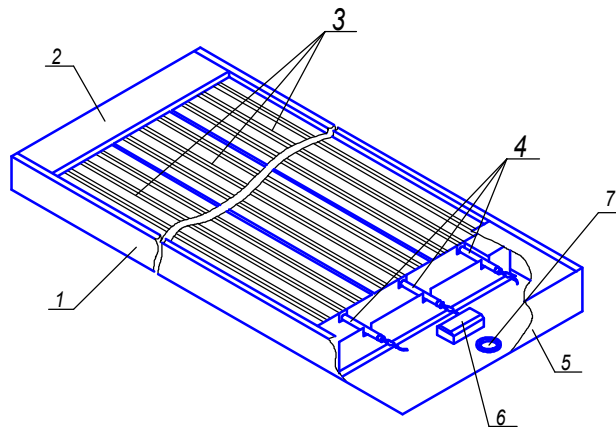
б Обогреватель ОИ-3 (ОИ-4)
